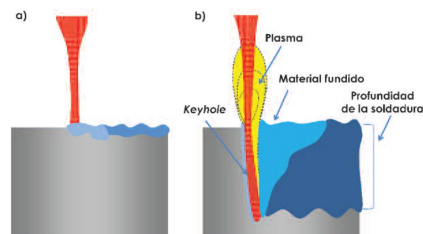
Tipos de soldadura láser. a) Limitada por conducción. b) Soldadura de penetración.
